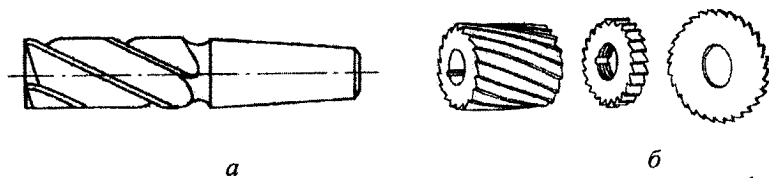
Цільні фрези: *а* – кінцева фреза, *б* – циліндрична і дискова фрези
